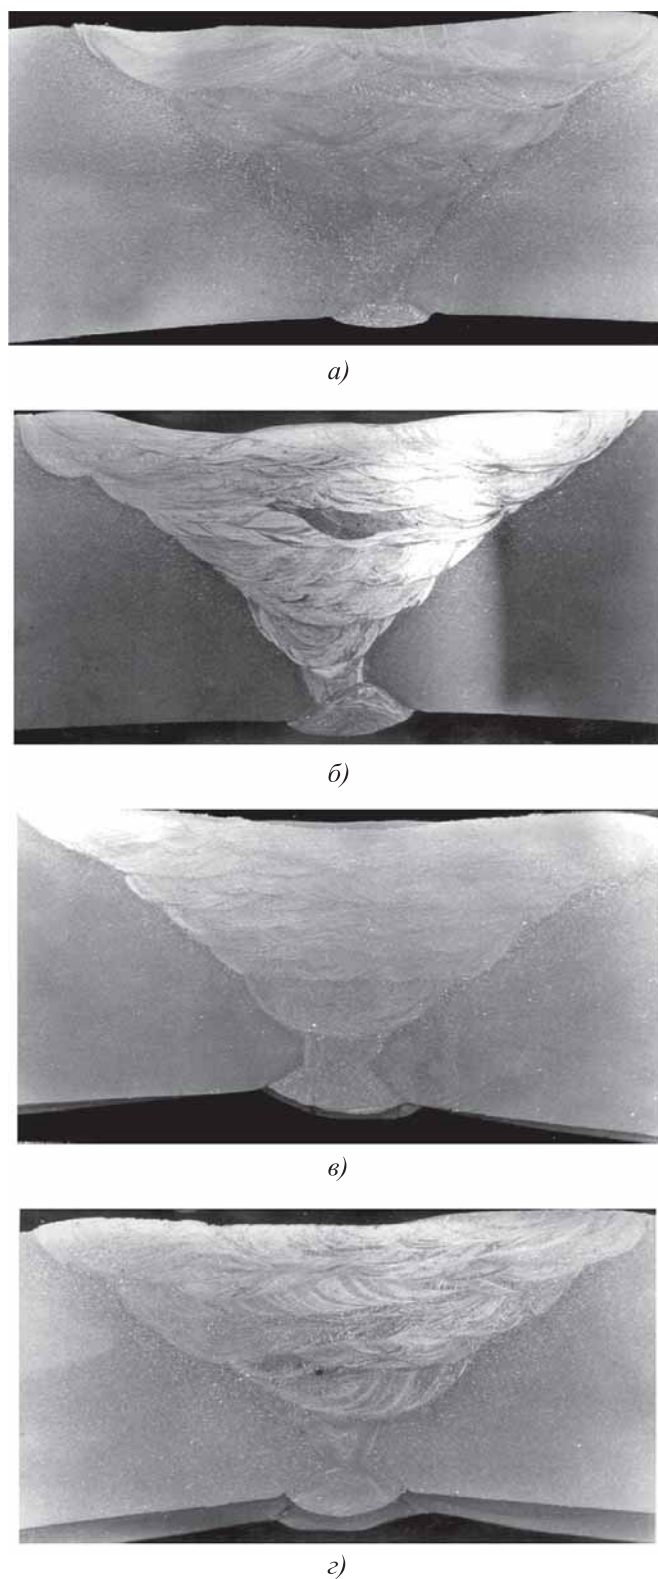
Макроструктуры стыковых соединений плит из сплава 1420 при ручной многопроходной сварке с различными присадочными проволоками ($\times 2,5$):
